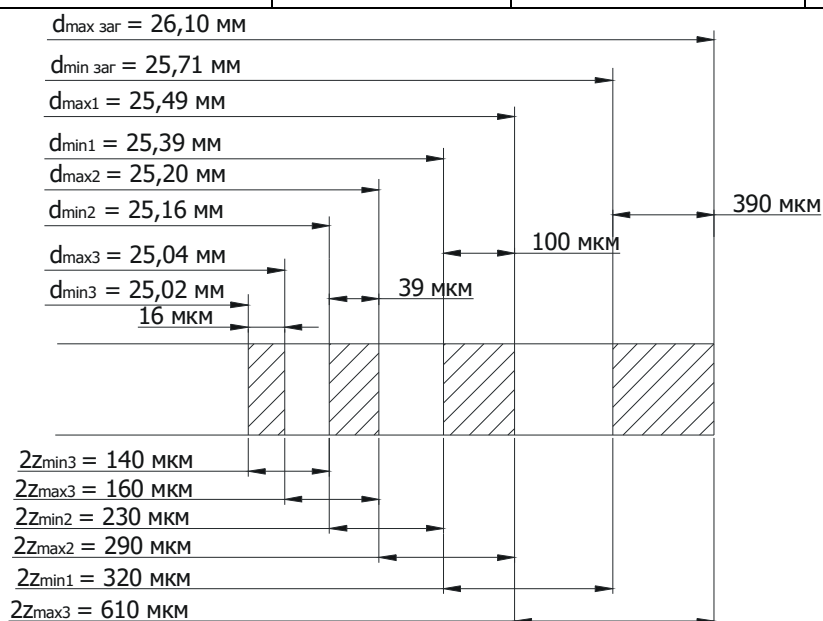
Схема графічного розміщення припусків і допусків на поверхню Ø 25 к6.
